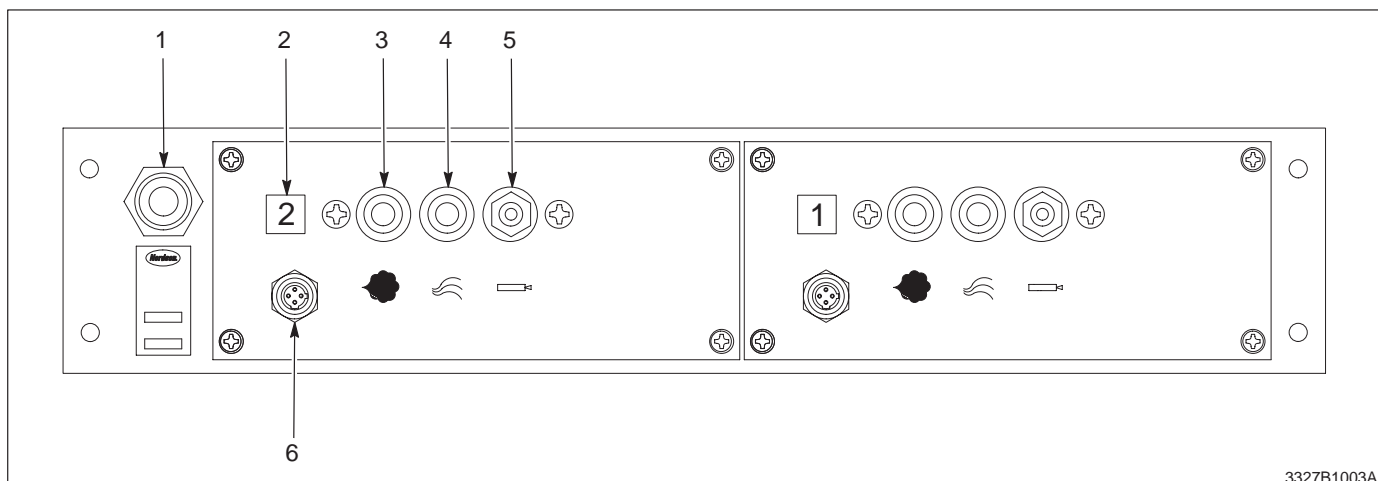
Rückwandanschlüsse des Pneumatikmoduls
